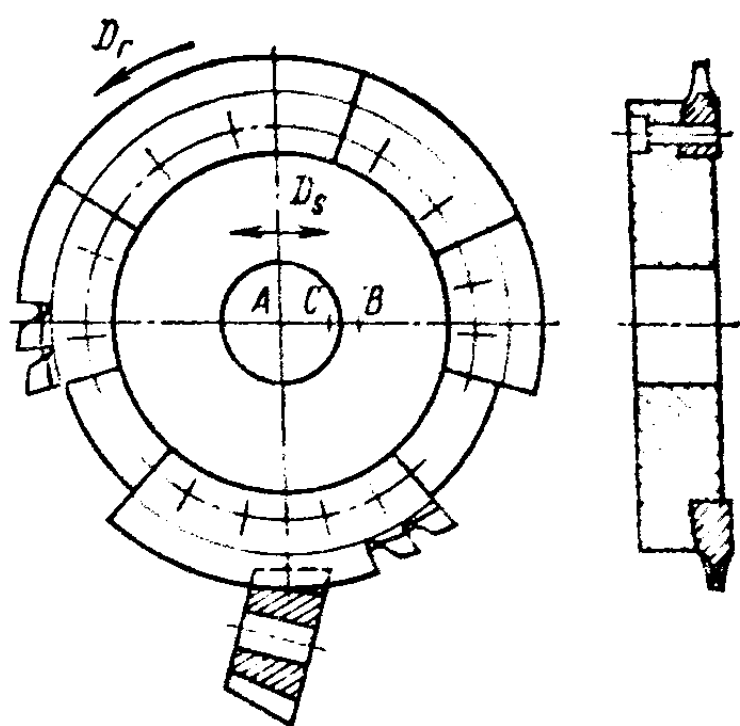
Схема обработки конического прямозубого колеса фрезой-протяжкой
